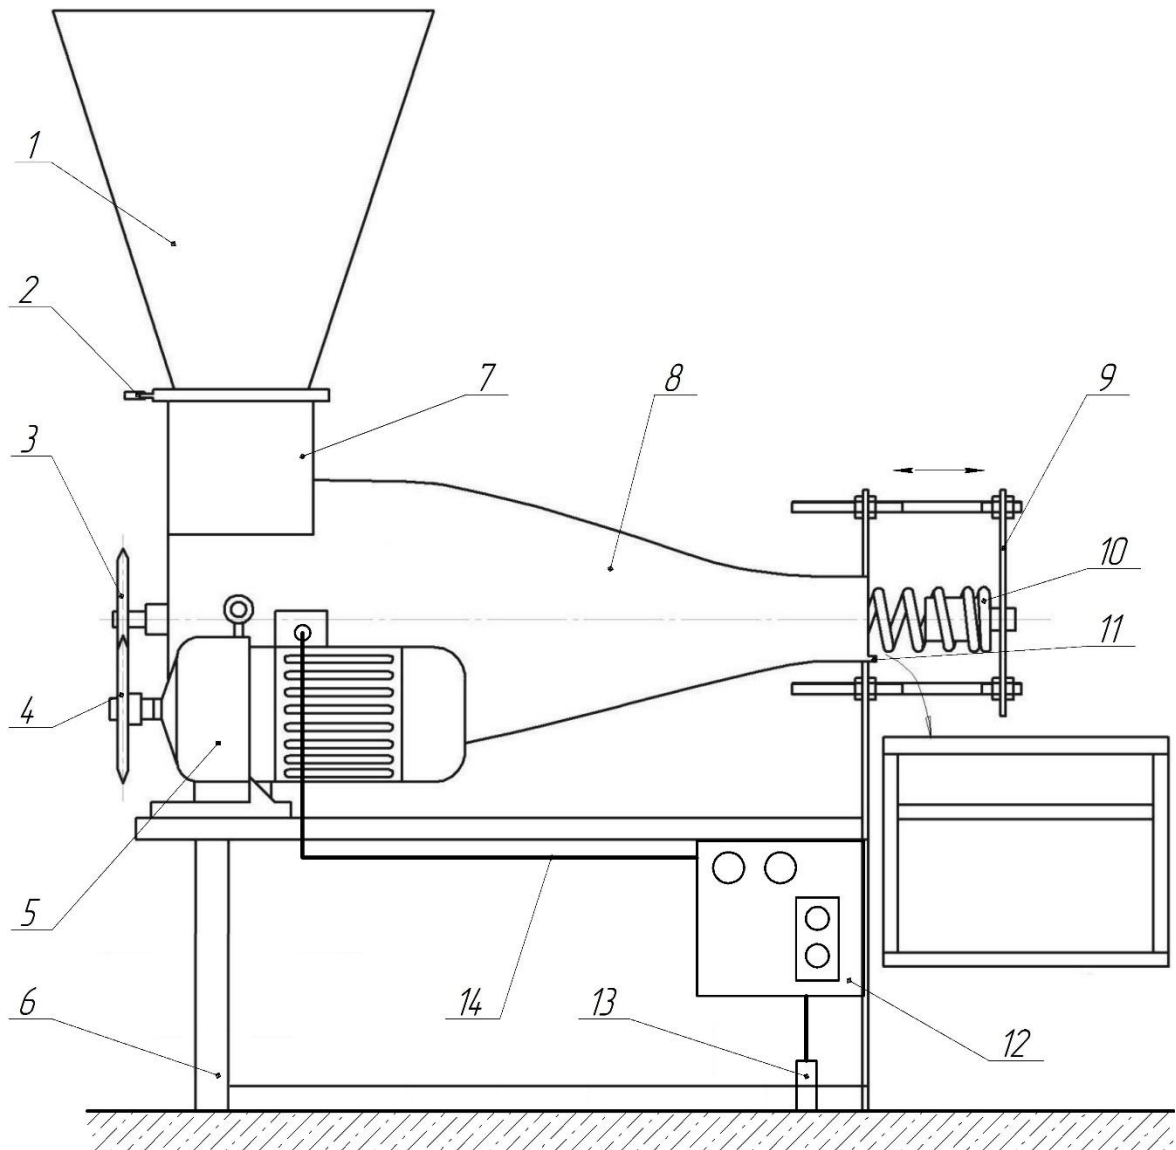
Вузли, які потребують певної уваги з точки зору безпеки праці оператора: 1 – приймальний бункер; 2 – регулювальна засувка; 3, 4 – зірочки ланцюгової передачі приводу; 5 – мотор-редуктор; 6 – рама; 7 – завантажувальна горловина; 8 – корпус бункера; 9 ведена цапфа; 10 – спіраль; 11 – вивантажувальна горловина; 12 – шафа керування; 13 – заземлення; 14 – електрокабель
